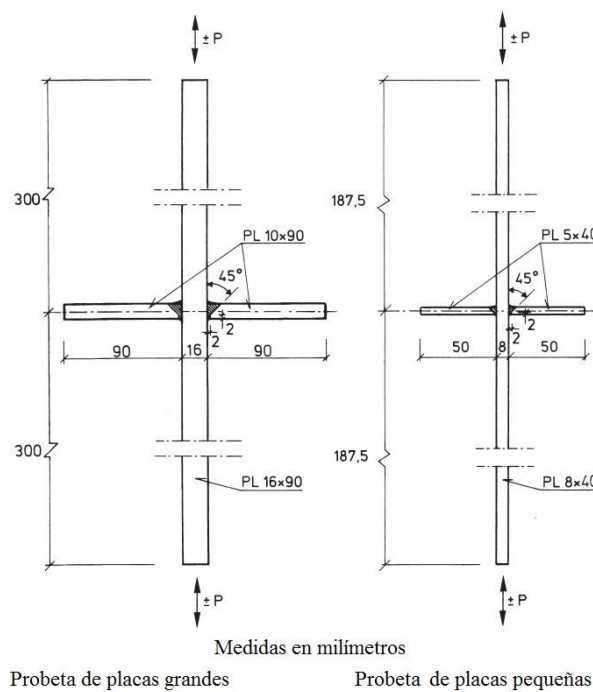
Probetas de placas soldadas con refuerzos transversales [44].
